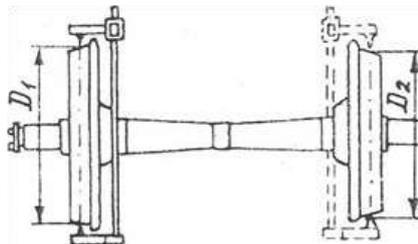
Положение штангенциркуля при измерении диаметров колес по кругу катания.
